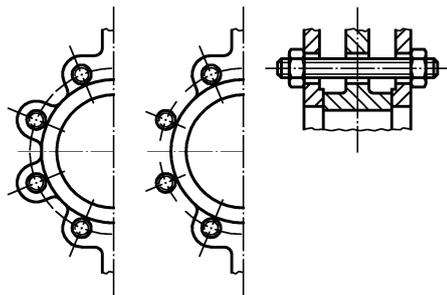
Einklemmklappe mit Flanschaugen und Durchgangsbohrungen
